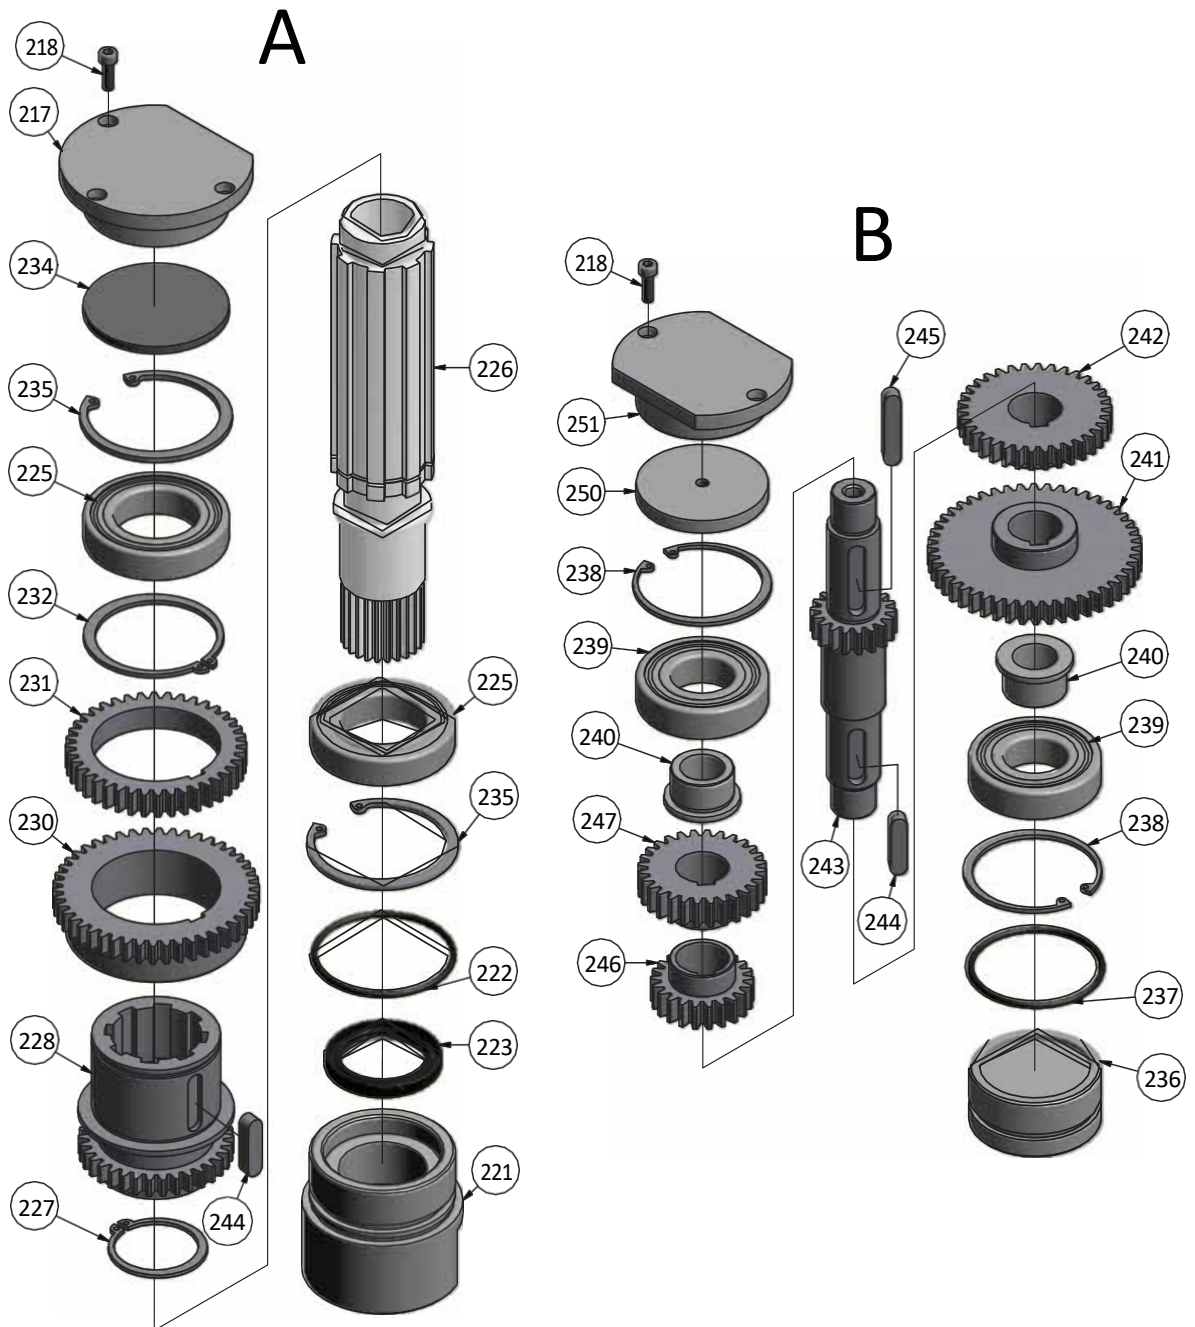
Getriebe Bohrspindel 1 von 4 - Gearbox main spindle 1 von 4
